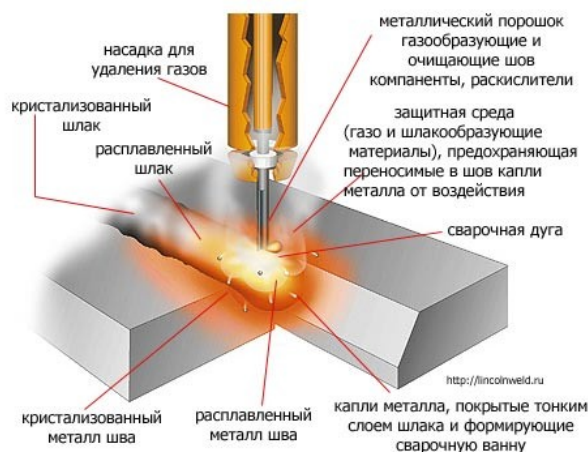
Схема автоматической сварки порошковой самозащитной проволокой
